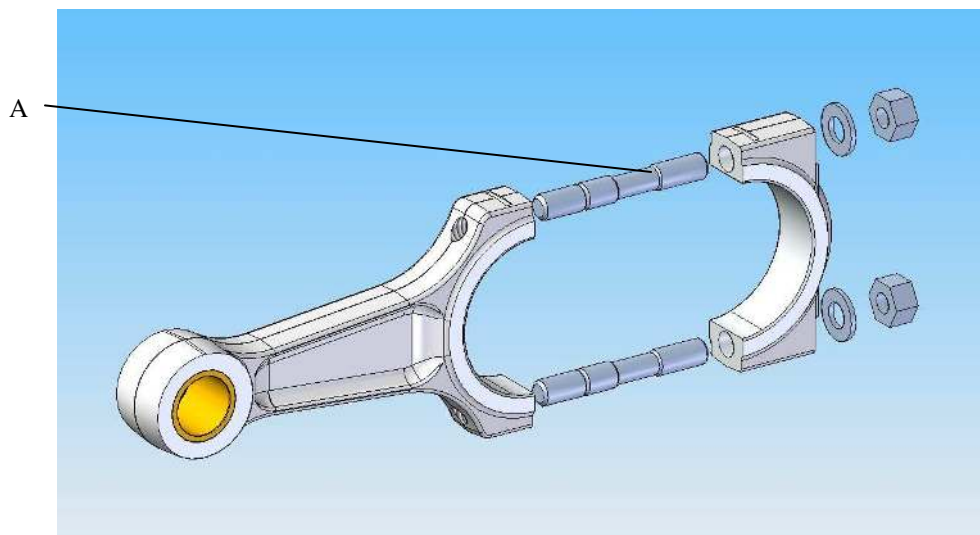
Детали шатунов для компрессоров SP4L1500..2500 SP4H2200..3500 и всех моделей с 6 и 8 цилиндрами
